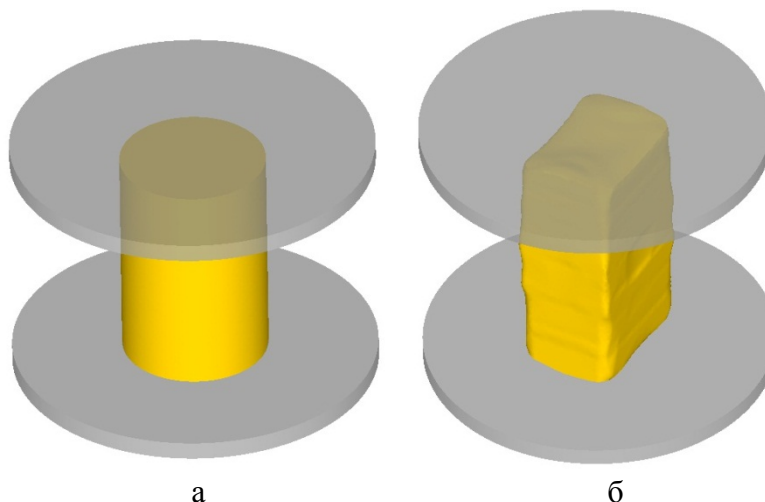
Схема осадки цилиндрической (а) и профилированной (б) заготовки
